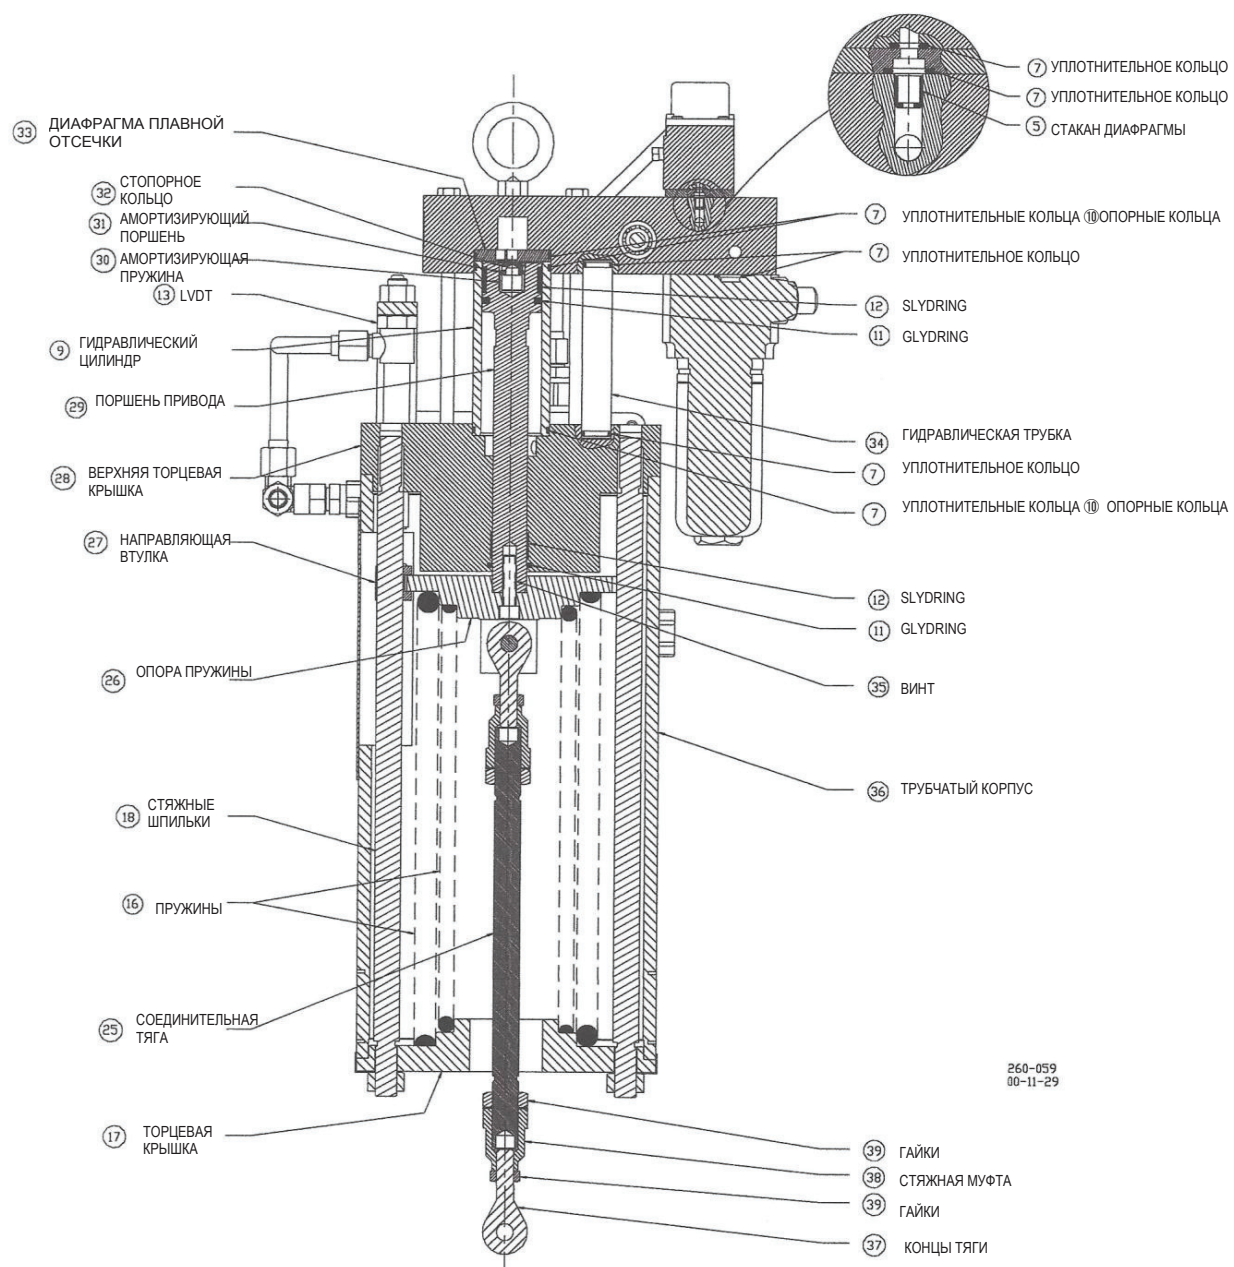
Запорно-регулирующий газовый клапан (малый привод, частичный разрез)
